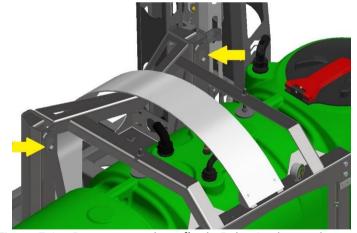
Pontos para elevação do Pulverizador na descarga.
